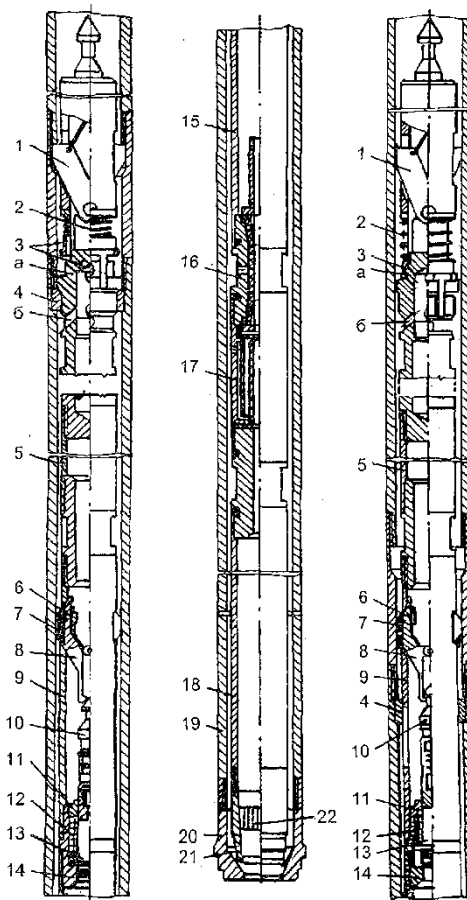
Съёмный керногазонаборник СКГН-76А ПГО "Запсибгеология": 1 - защелка; 2 - пружина; 3 - втулка; 4 - кольцевая опора; 5 - удлинитель; 6 - стопор; 7 - фиксатор; 8 - захватная лапа; 9 - корпус захватного узла; 10 - головка с грибком; 11 - втулка; 12 - пружина; 13 - клапан; 14 - корпус клапана; 15 - газосборник (колокол); 16 - соединительный элемент; 17 - водяной затвор; 18 - керноприемник; 19 - наружная колонковая труба; 20 - буровая коронка; 21 - стакан (штамп); 22 - кернорватель
